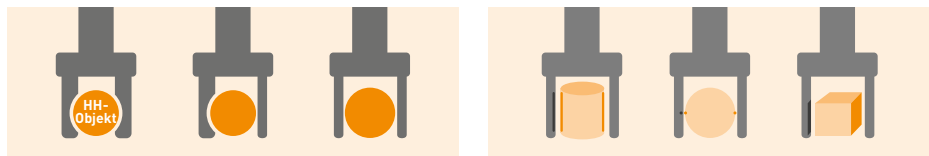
(links) Formschluss, Form-Kraftschluss, Kraftschluss, (rechts) Linienkontakt, Punktkontakt, Flächenkontakt
